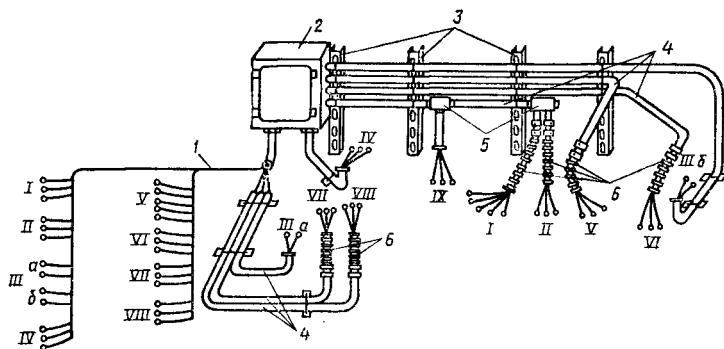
Блок электропроводки для тележки мостового крана:
